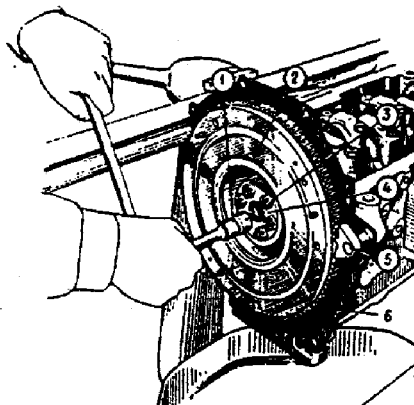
Desmontagem do volante: 1 - soquete; 2 - volante; 3 - parafuso de fixação do volante; 4 - arruela; 5 - dispositivo de retenção do volante nº A.60330/R; 6 - placa dianteira da carcaça da embreagem.
